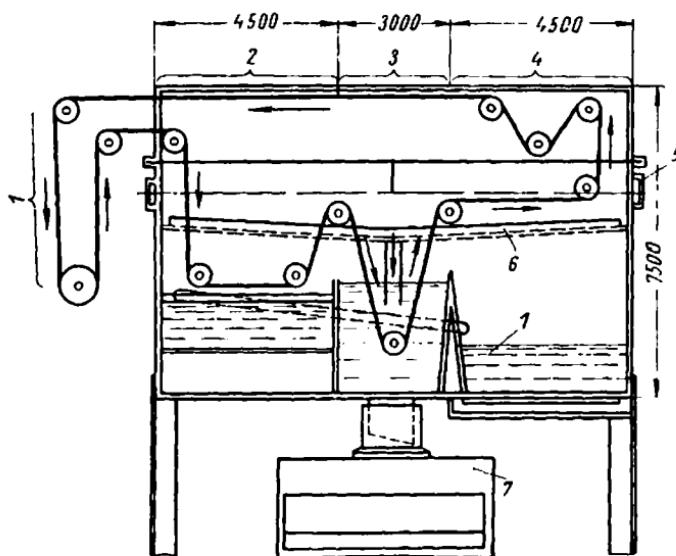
Схема агрегата для очистки отливок с помощью ультразвука:
